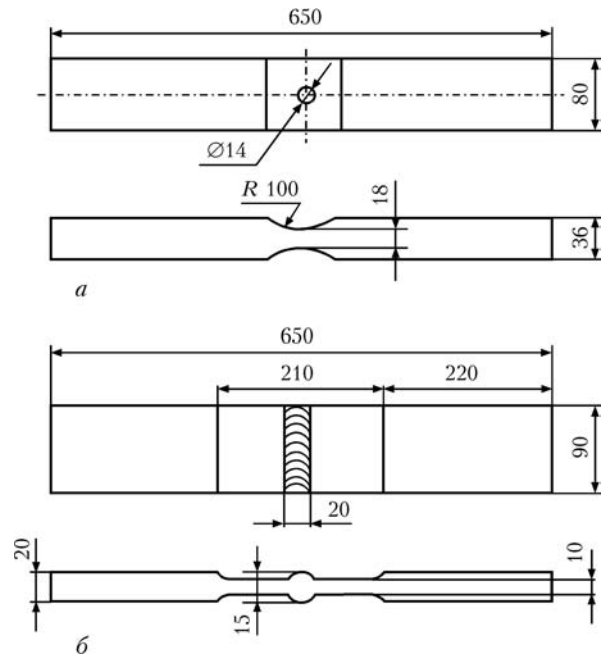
Схемы образцов для усталостных испытаний при одно- и поличастотном нагружении из основного металла с центральным отверстием (а) и со стыковым сварным соединением (б)
